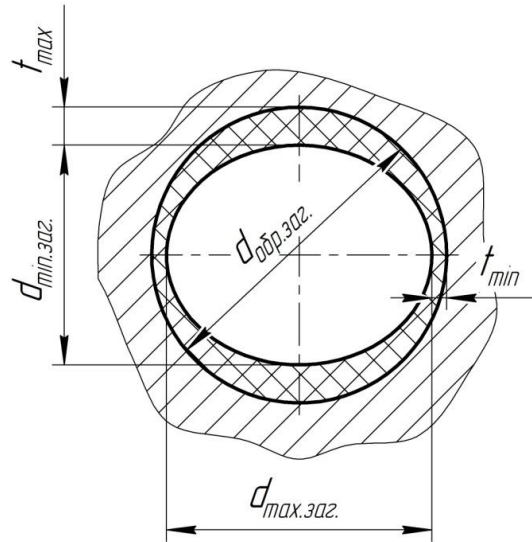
Схема образования неравномерности припуска от предварительной овальности заготовки
